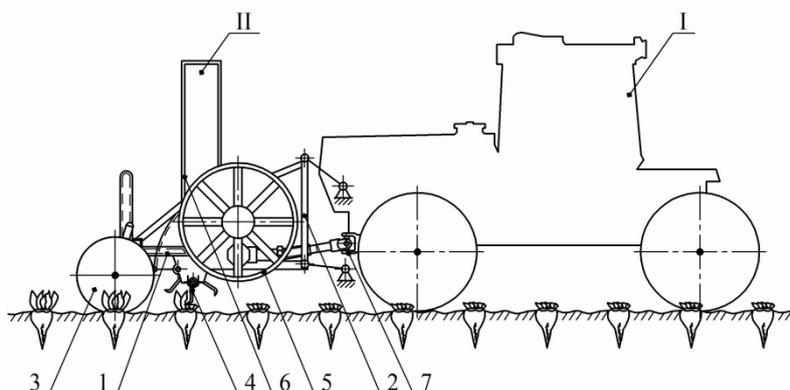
Ботвоуборочный агрегат для уборки ботвы сахарной свеклы:
